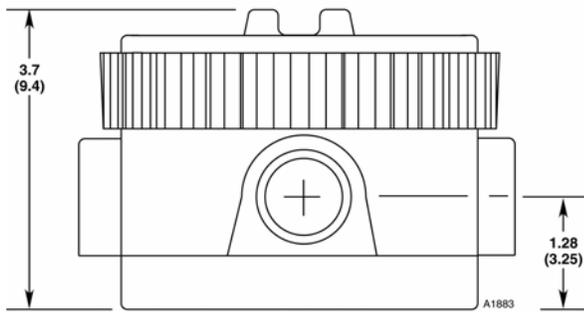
Габаритные размеры соединительной коробки с низкой крышкой в дюймах (см).
